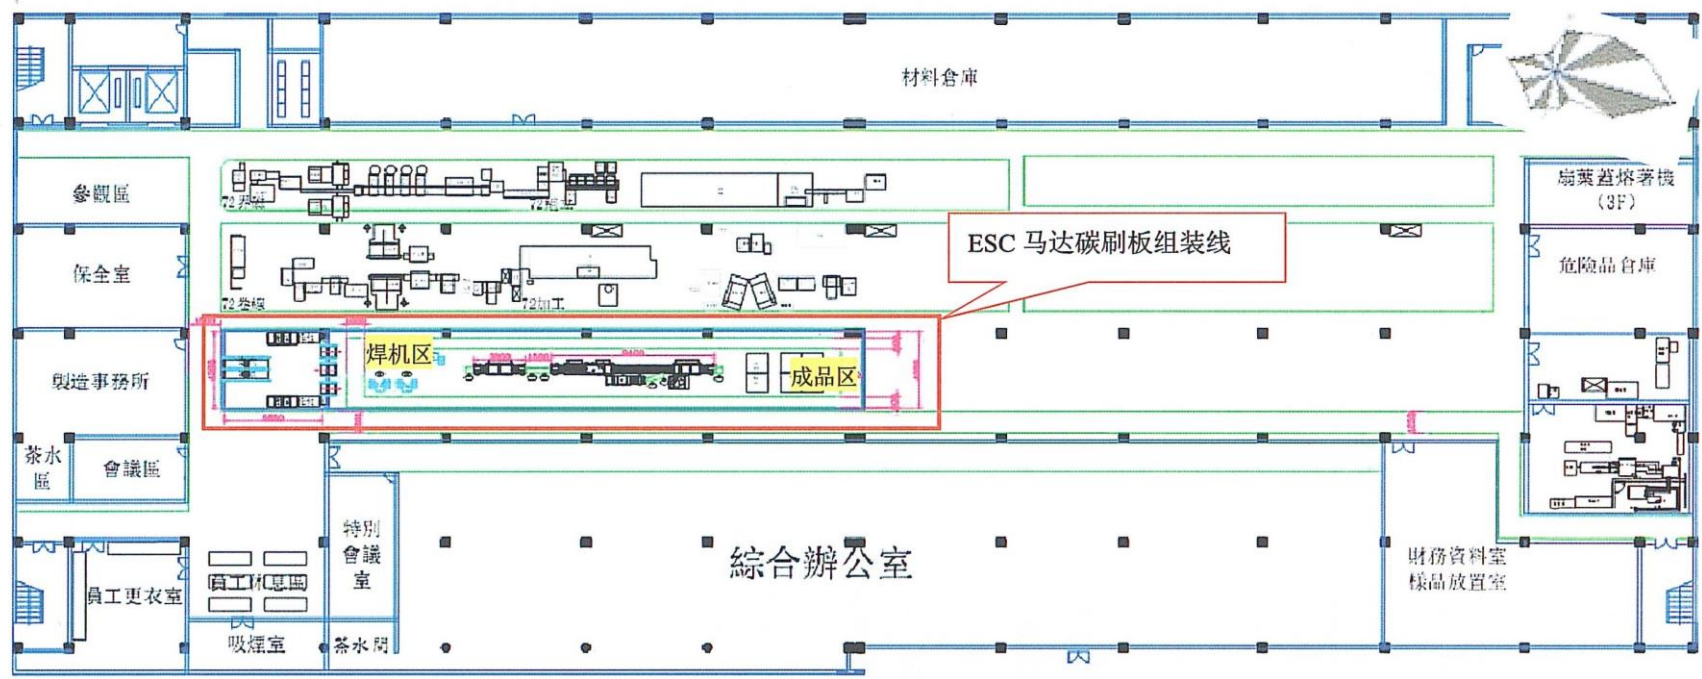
厂区 A 栋 2 楼吸尘器马达生产车间平面布置图
